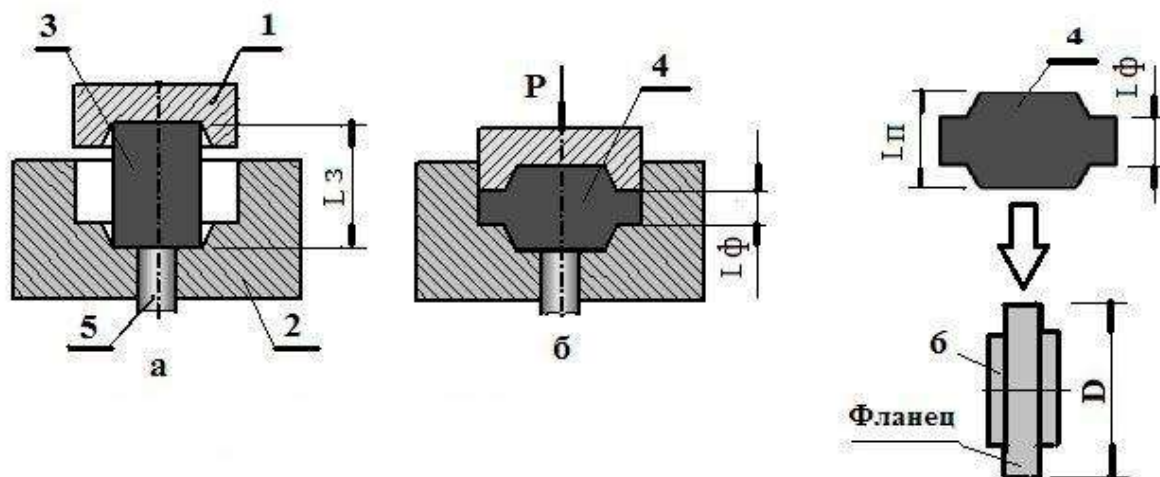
Схема гарячого об'ємного штампування у закритому штампі: 1 – верхня половина штампі; 2 – нижня половина штампі; 3 – вихідна заготовка; 4 – готова заготовка; 5 – виштовхувач; 6 – деталь, яка отримана із заготовки.
